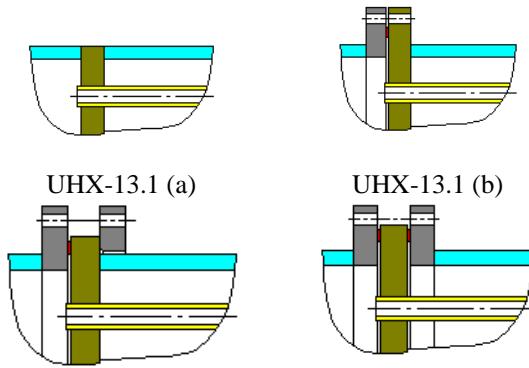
Крепление трубной решетки по ASME VIII-1
